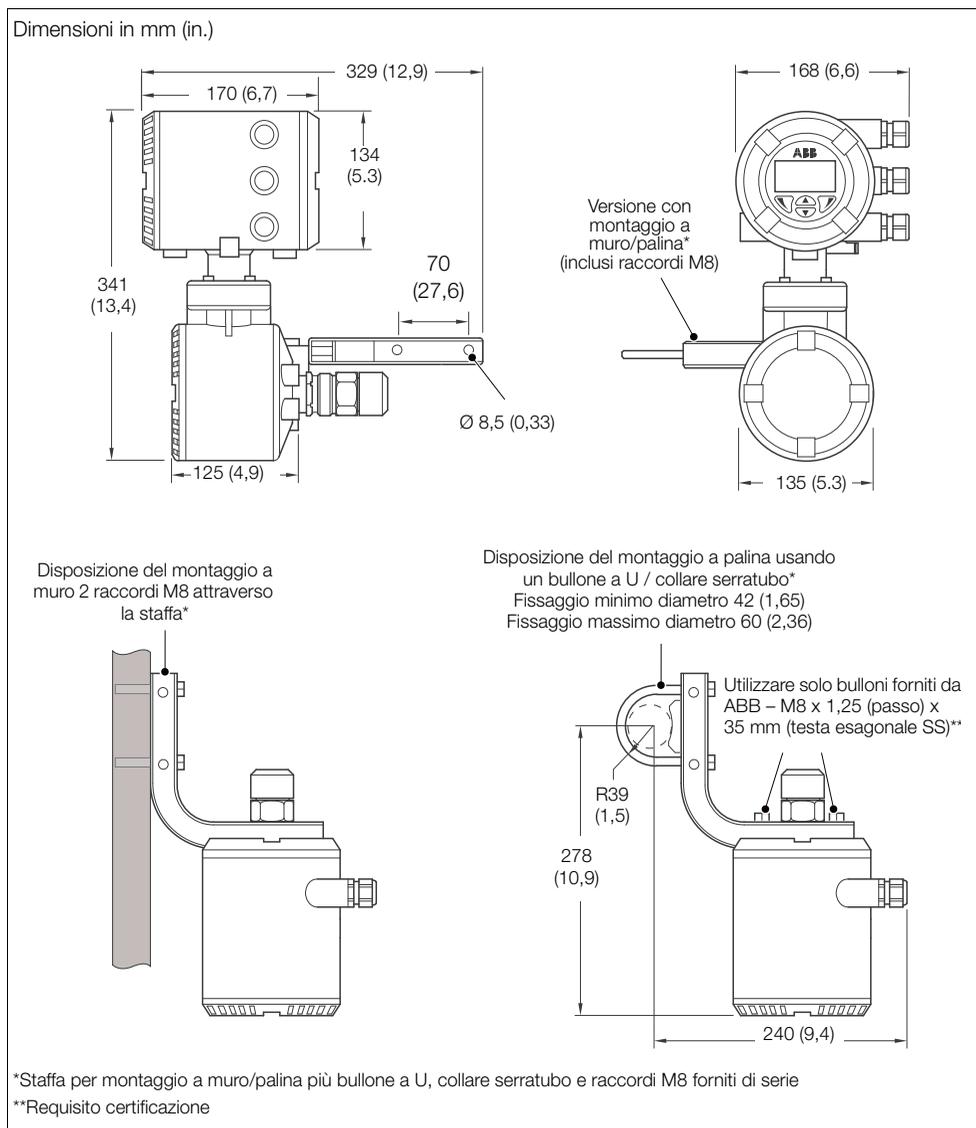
Dimensioni complessive – Trasmettitore remoto
